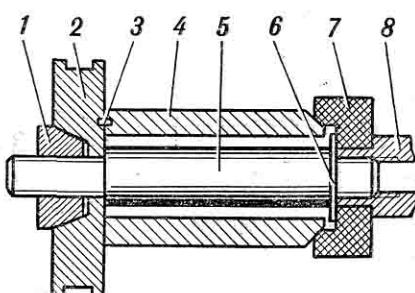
Установка пускового шкива на торец коленчатого вала: 1 — конусная гайка, 2 — шкив, 3 — шпилька, 4 — втулка, 5 — ось, 6 — шайба, 7 — гайка, 8 — шейка коленчатого вала.
